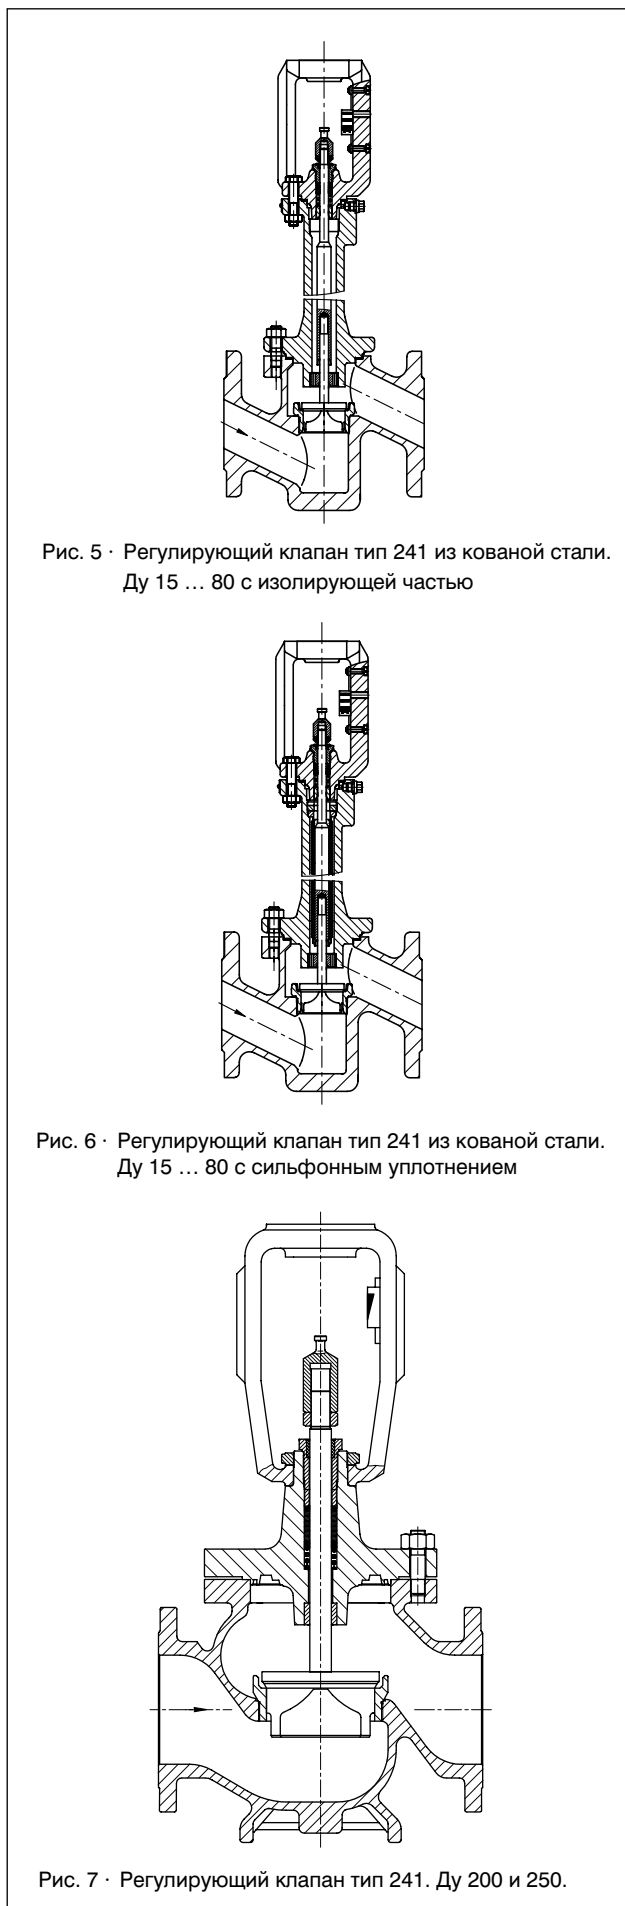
· Регулирующий клапан тип 241 из ковanej стали.
